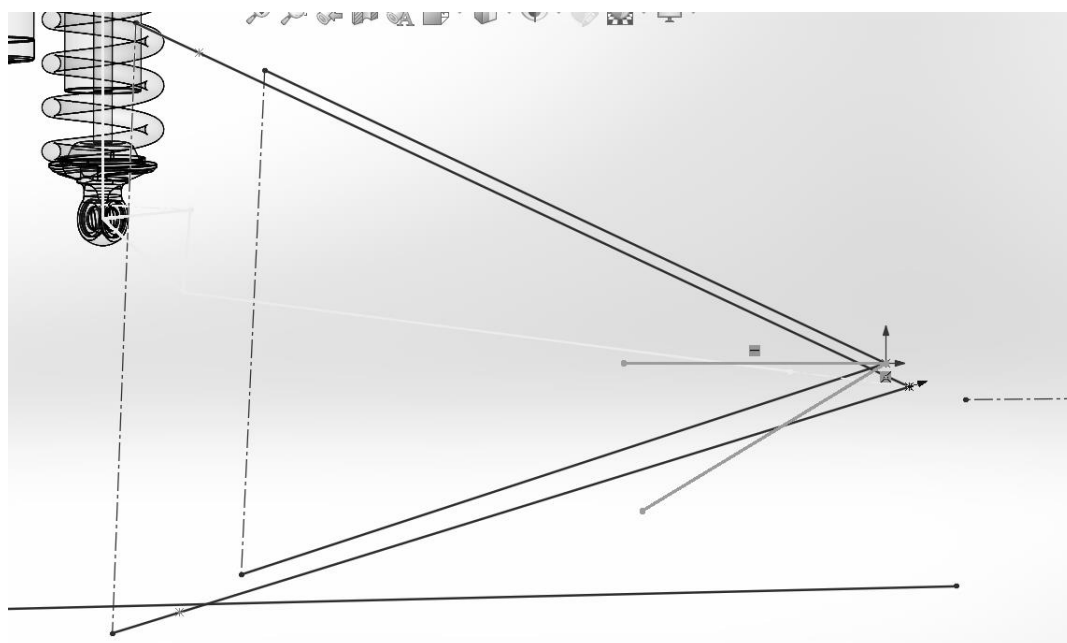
Компоновочный эскиз рычага перед привязкой к компоновочному эскизу передней подвески
